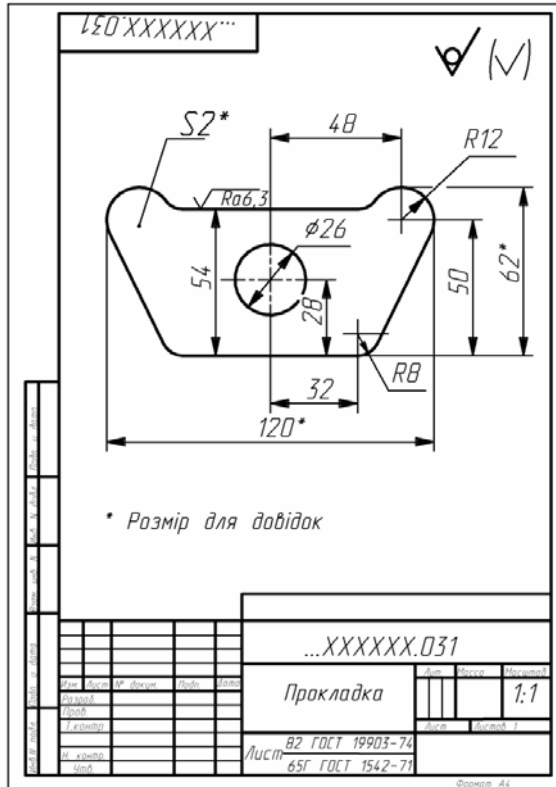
Кресленник плоскої симетричної деталі з листового матеріалу
